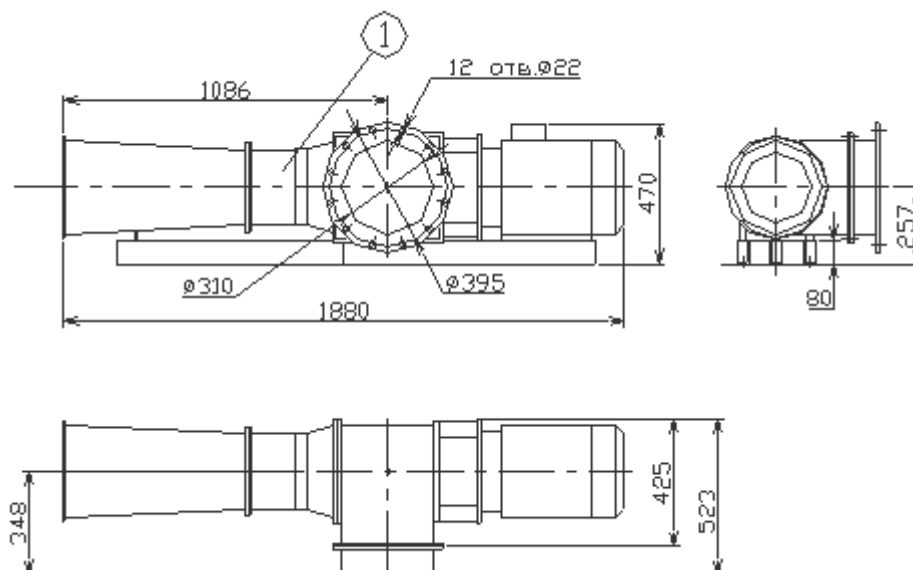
Габаритные, установочные и присоединительные размеры МикроГЭС 10Пр
